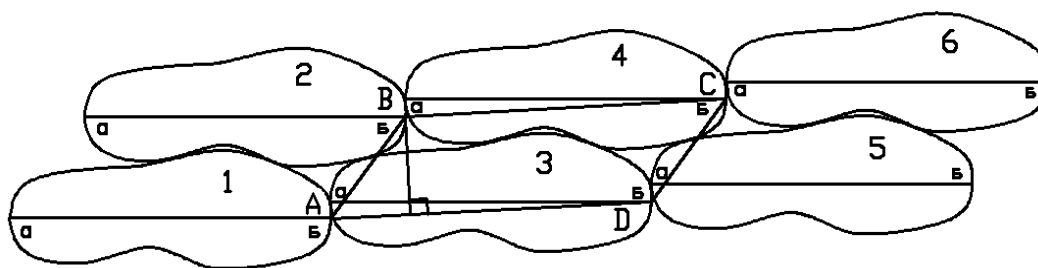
Схема совмещения подошв и стелек в одну сторону (вариант 3)
